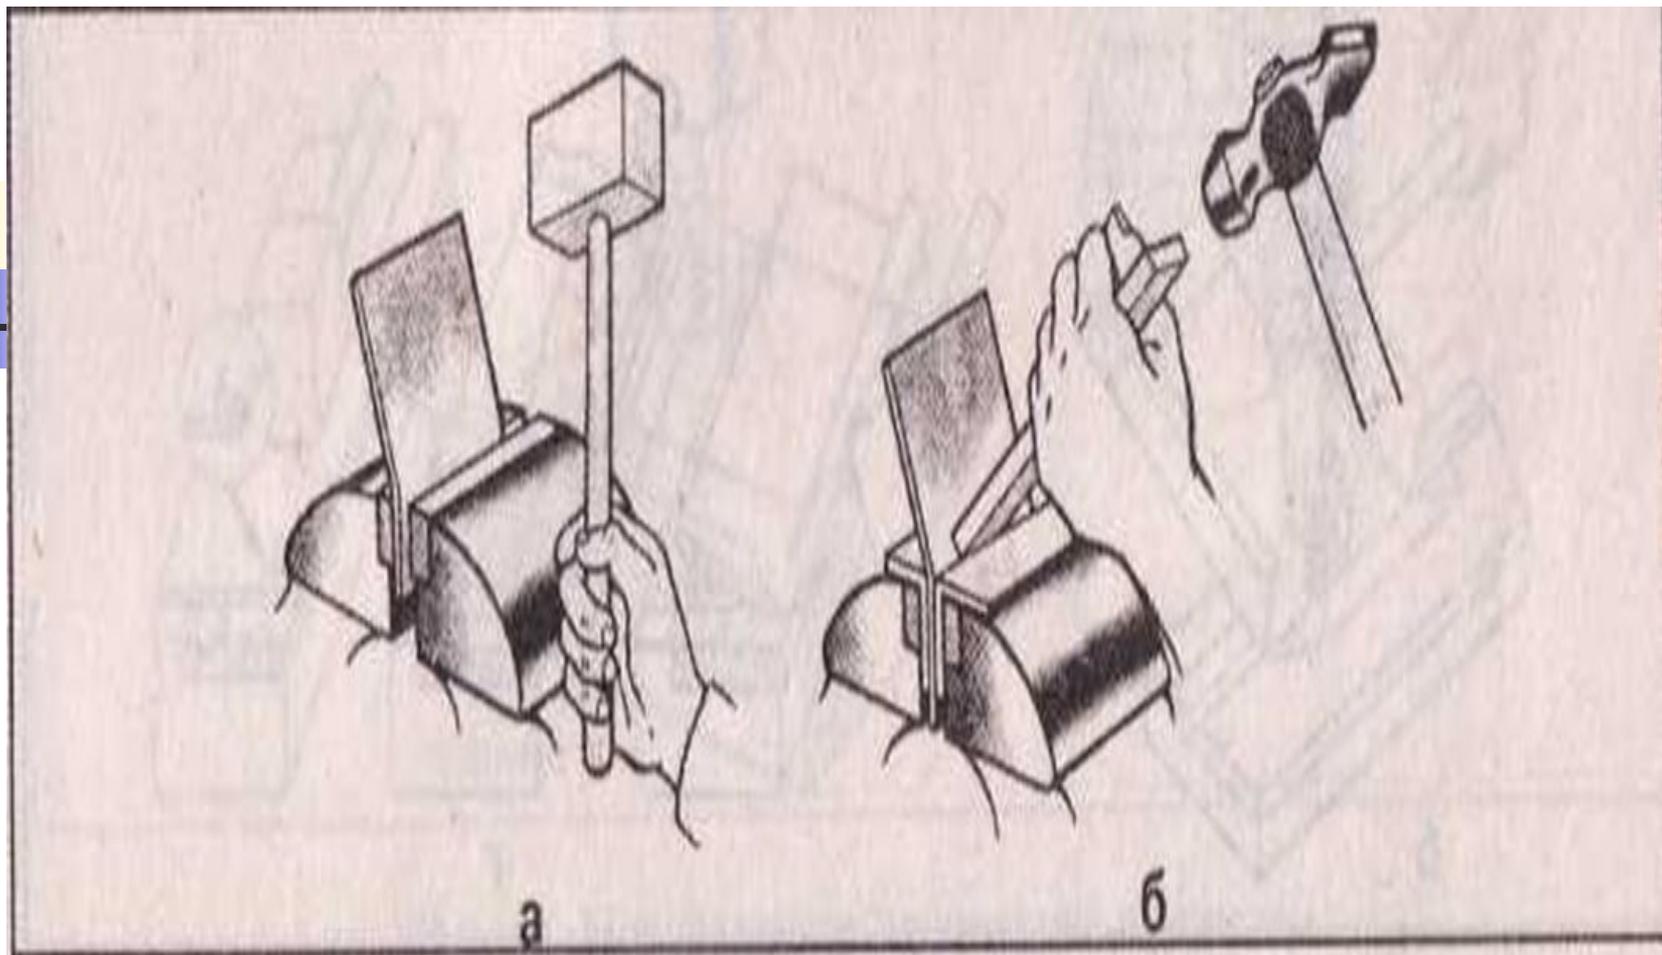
Сгибание заготовок из тонколистового металла в тисках:
